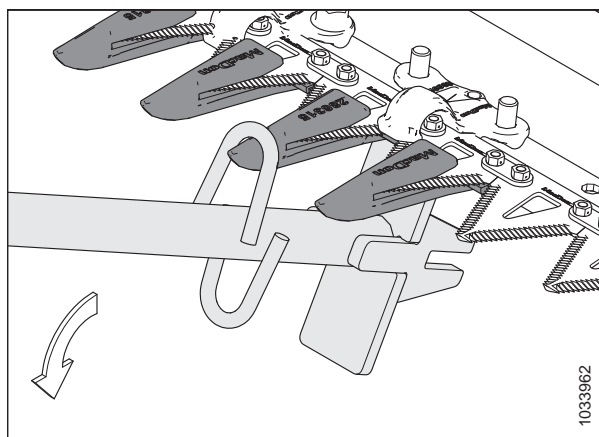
Регулировка смещением вниз — заостренный противорежущий палец
